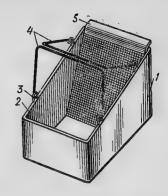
f* — корпус; 2 — отбортовка; 3 — проушина; 4 — руч-ки; 5 — сетка
